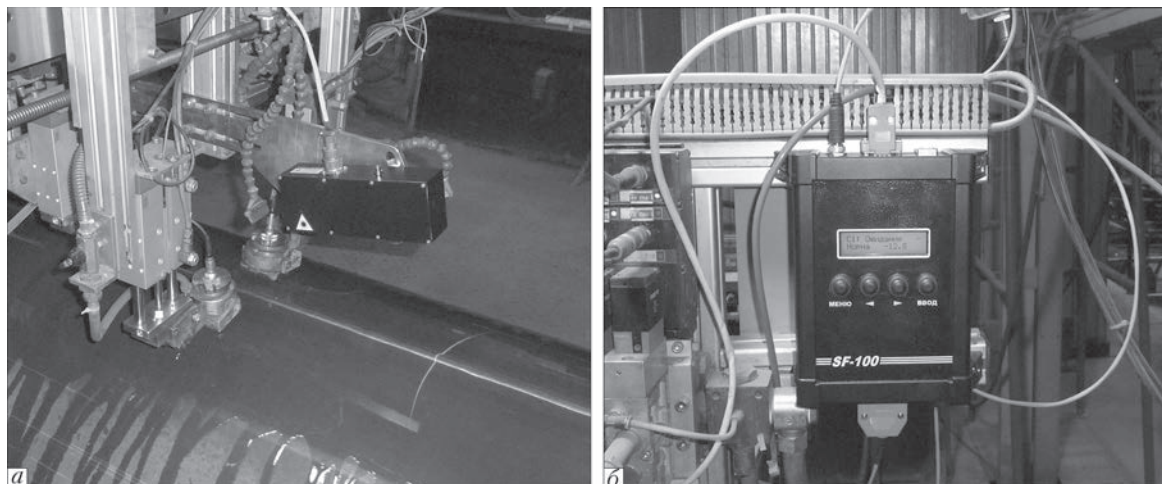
Система слежения за валиком усиления сварного шва на установке АУЗК: а – лазерный датчик на механоакустическом блоке; б – коммуникационный модуль
